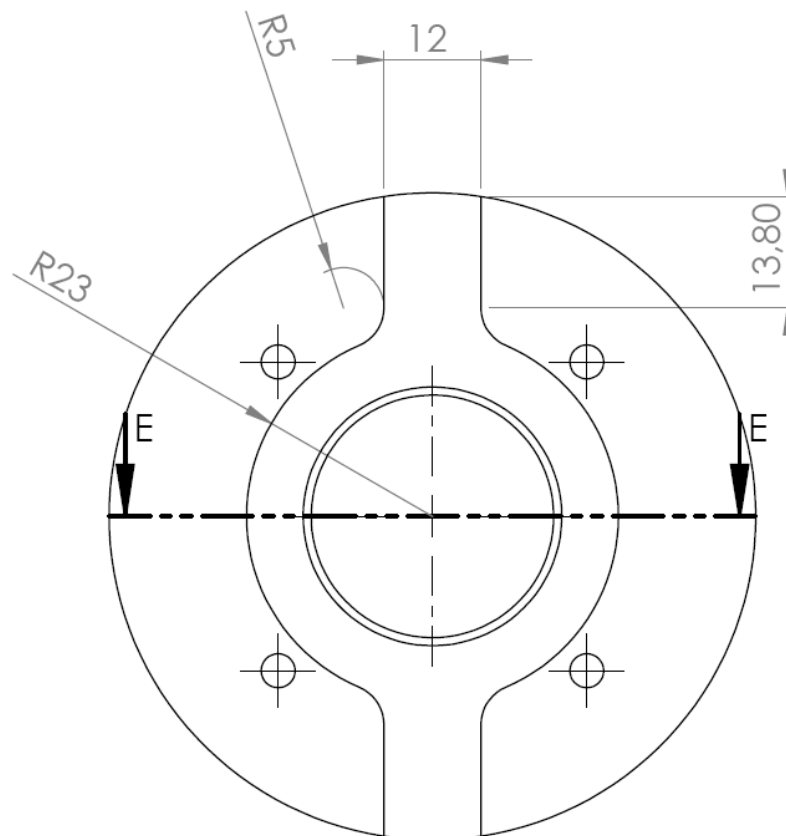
Parte superior do cabeçote - vista de cima (desenho 1)
